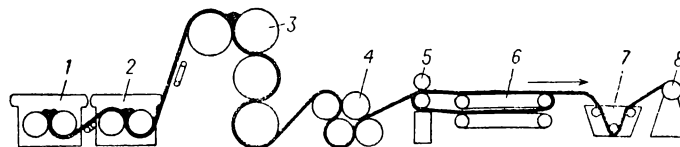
Схема изготовления дублированной заготовки для резиновых ковров:
